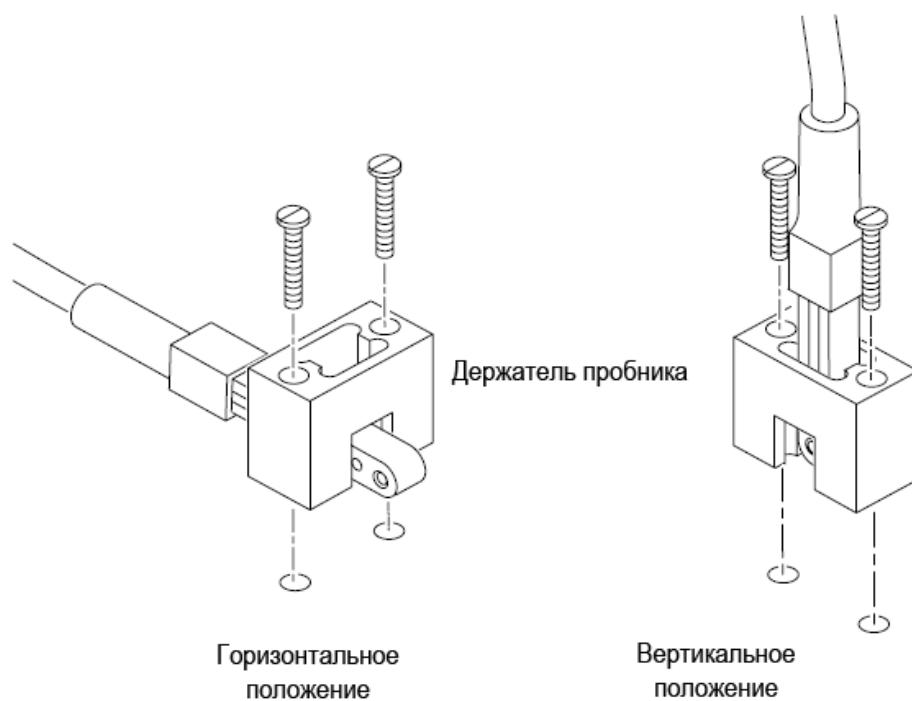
Крепление головки пробника СТ-6 к тестовой плате
